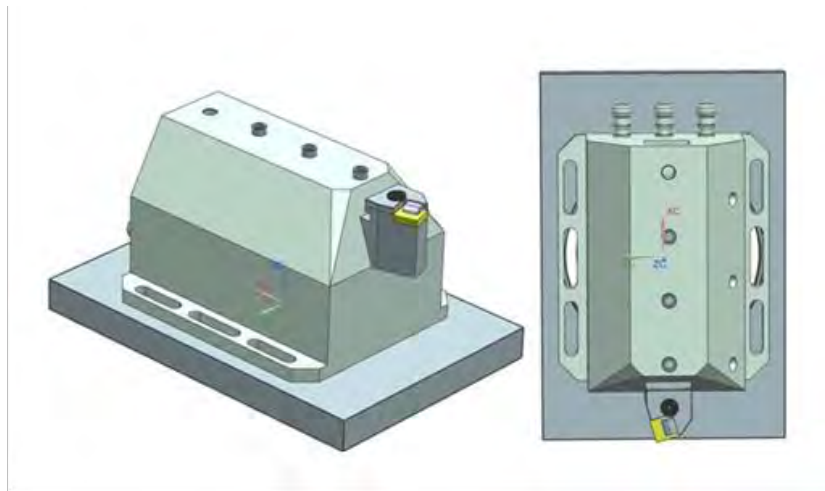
Izquierda; Vista isométrica dinamómetro KISTLER con accesorios, Derecha; Vista superior de dinamómetro con portaherramientas.
